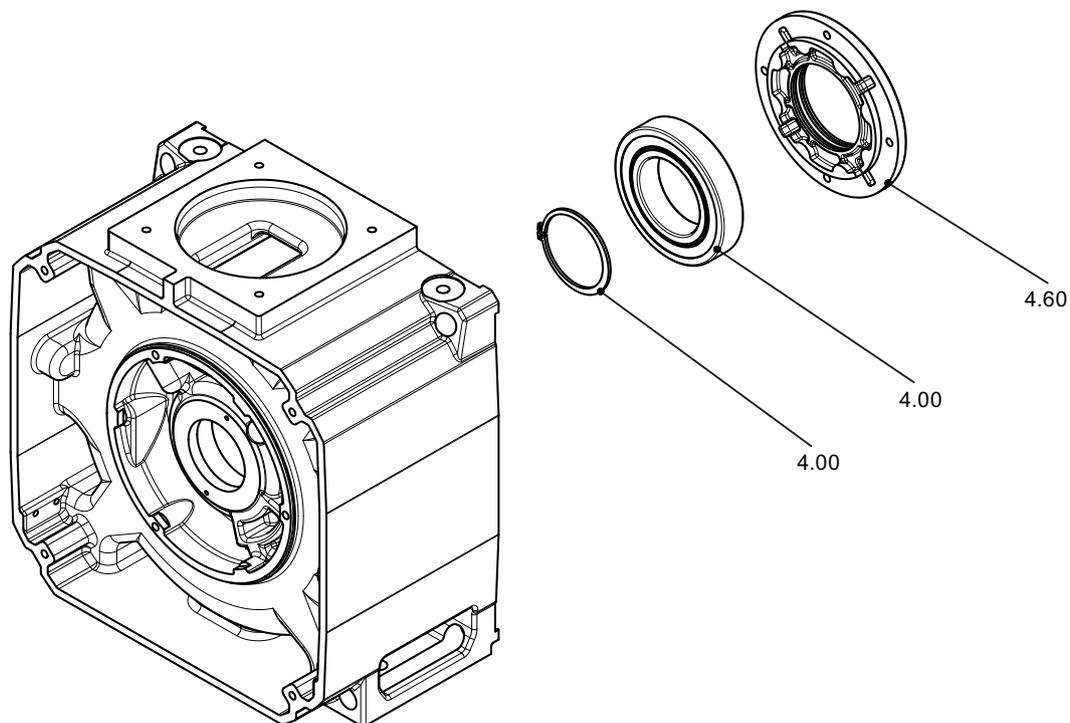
Узел подшипника качения неприводная сторона, непрерывная смазка
